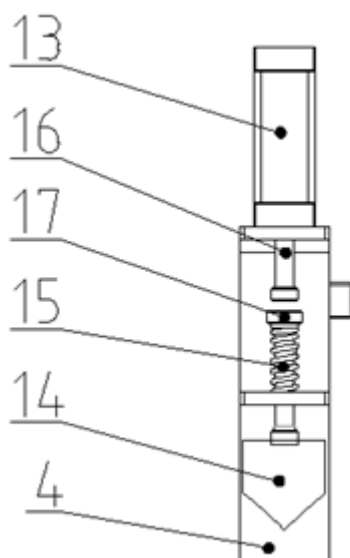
соединение пневмоцилиндра и фигурного ножа, вид спереди
